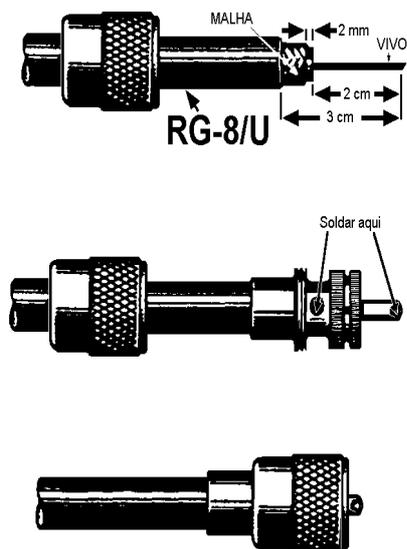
Detalhes da soldagem do conector coaxial ao cabo de alimentação
